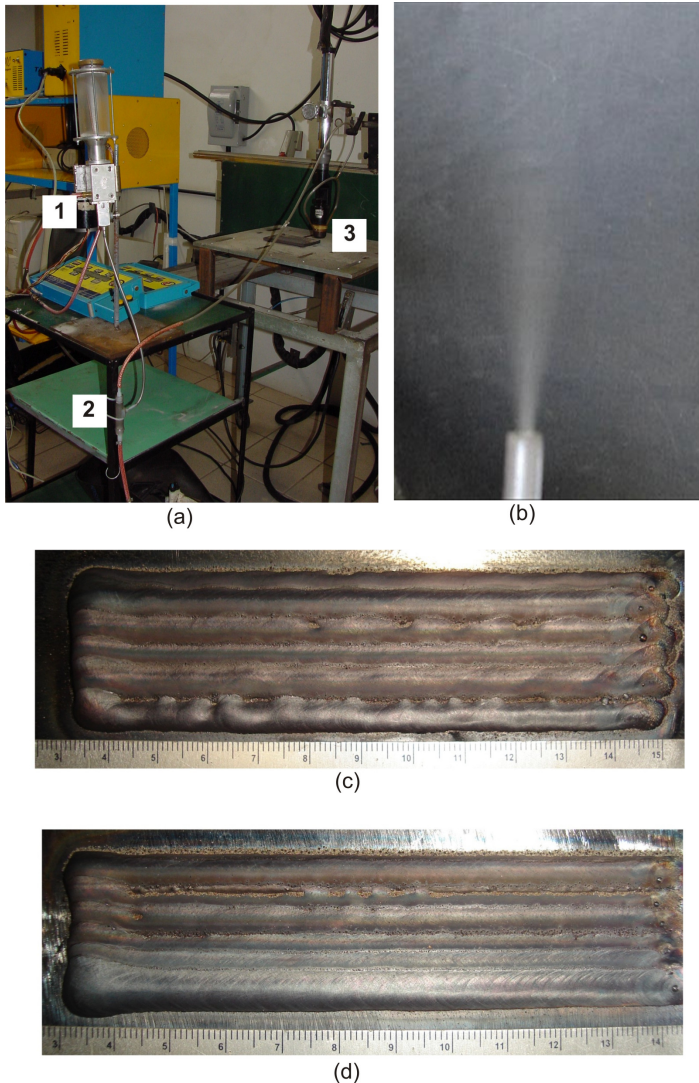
Soldagem envolvendo o Fluidizador: a) bancada de ensaios com 1- ADP de Fuso, 2- Fluidizador e 3- Tocha de Soldagem; b) aspecto do jato de partículas expelido pela mangueira de 2,0 mm; c) aspecto de um revestimento produzido sem Fluidizador; d) aspecto de um revestimento produzido com Fluidizador
